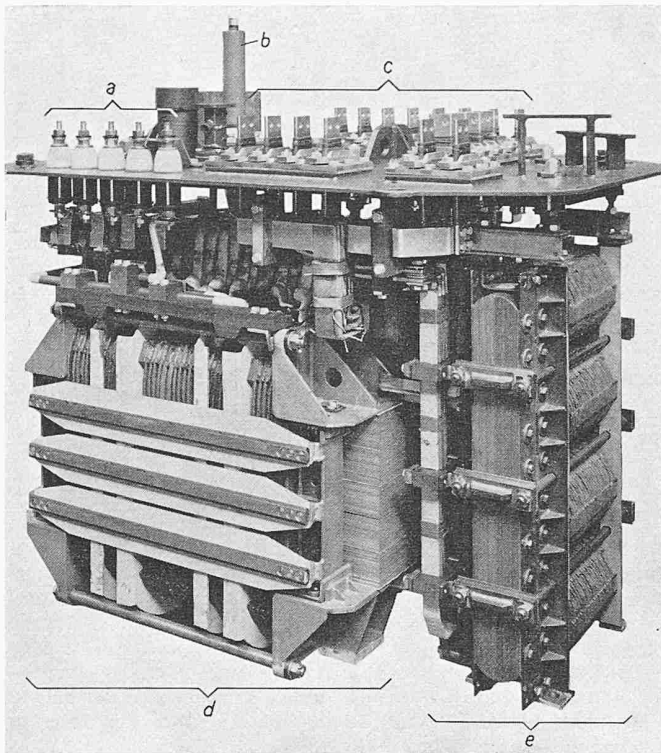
Ausgebauter Transformator mit Vierzweigdrossel
